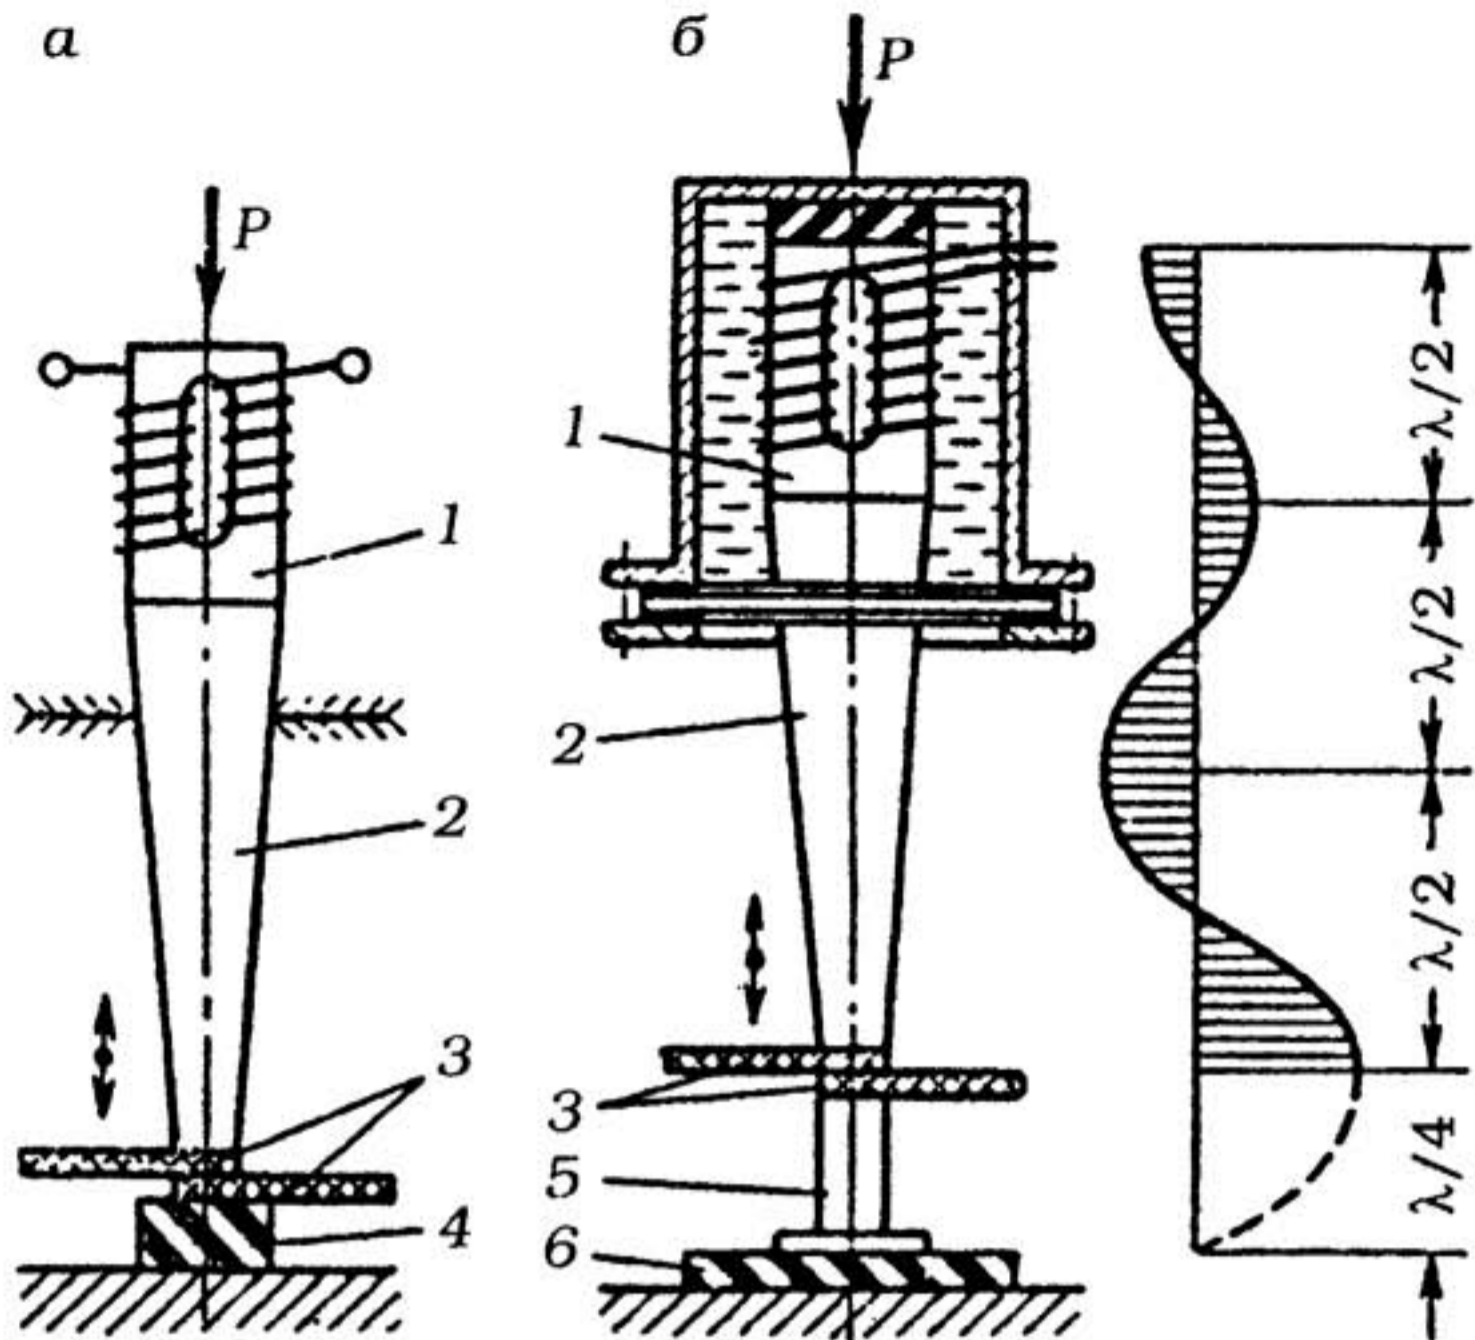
Схема ультразвуковой сварки с пассивным (ненастроенным) отражателем (а) и с активным отражателем (б):
